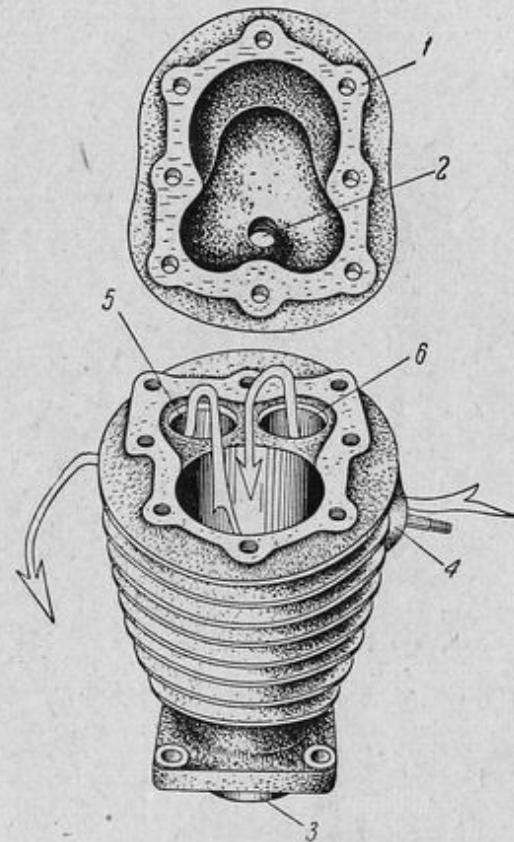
Цилиндр двигателя ТИЗ-АМ-600:
